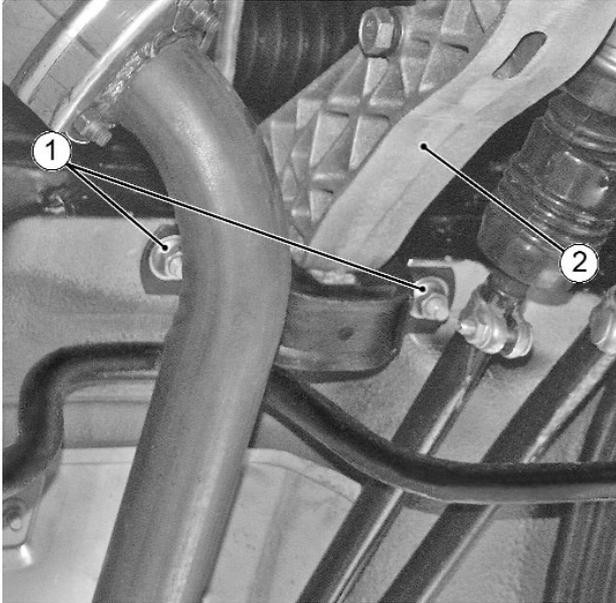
Отсоединение задней опоры подвески двигателя:
